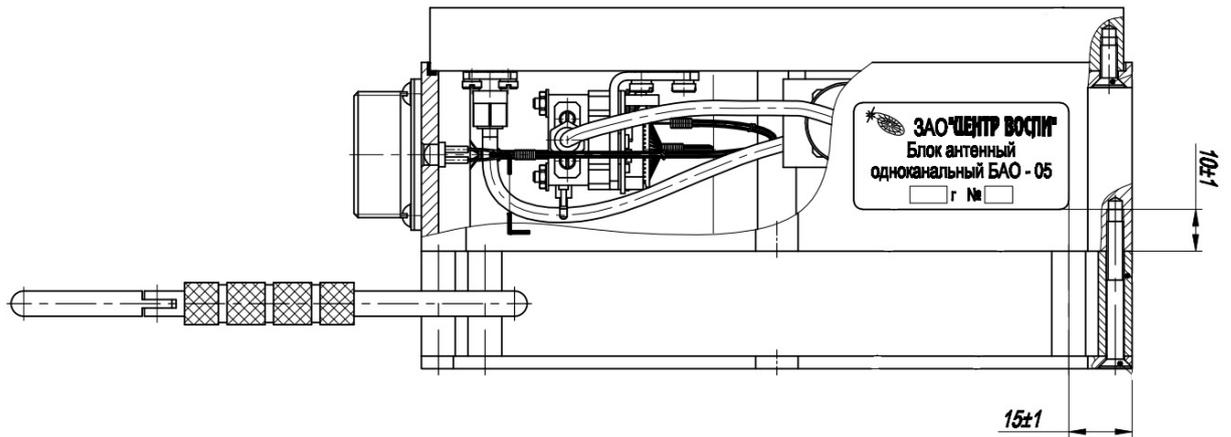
Внешний вид и установка шильдика на БАО-05
